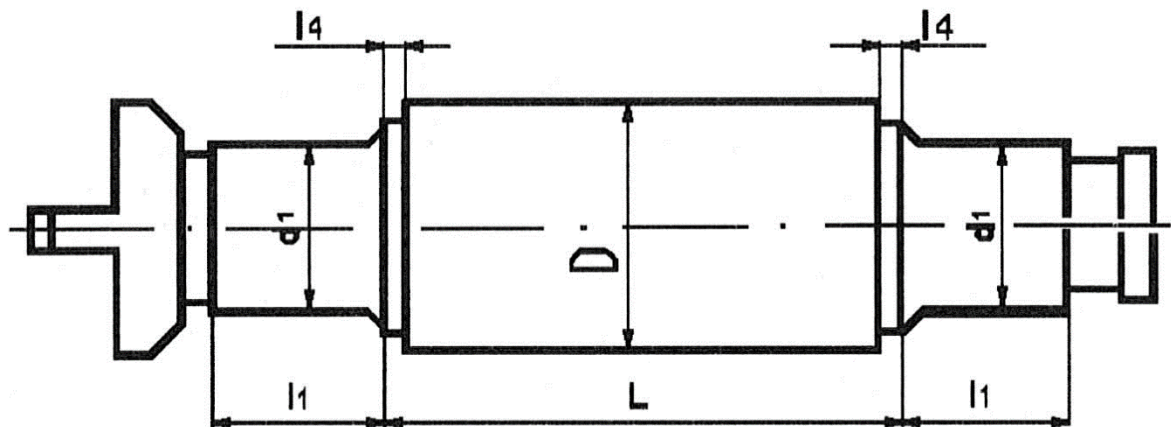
Валок стану дуо з підшипниками ковзання з текстолітовими вкладниками
